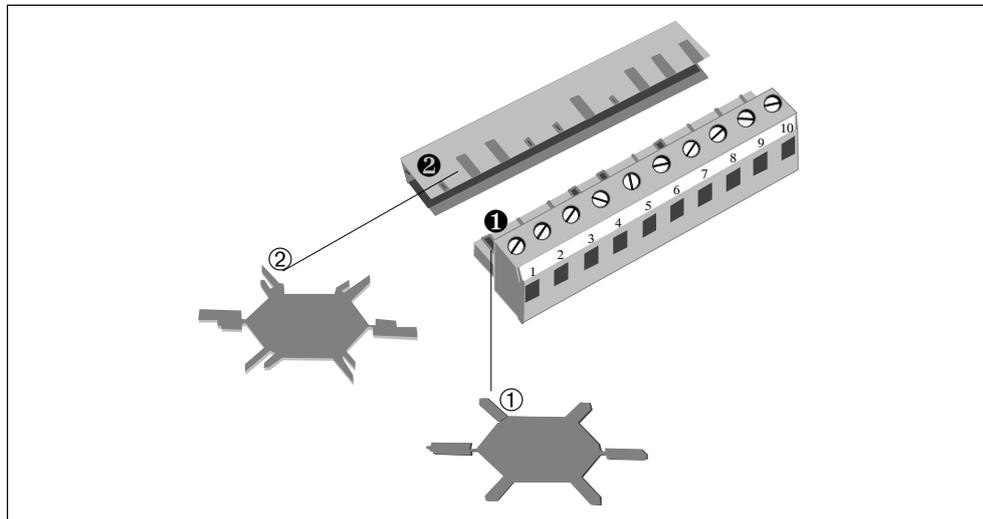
So werden Stecker unvertauschbar gemacht.
